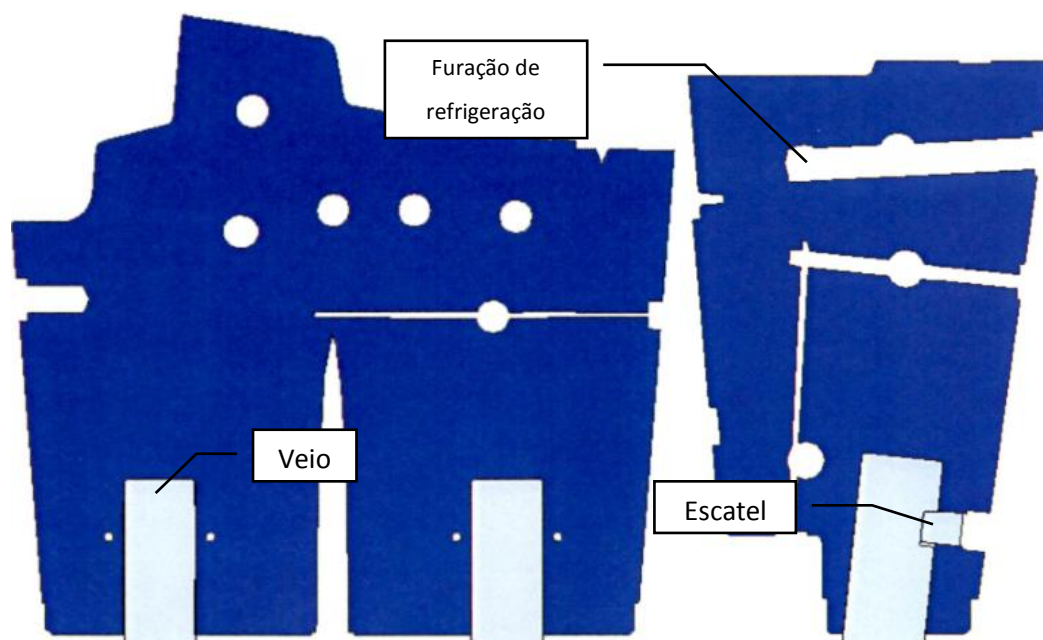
Vistas em corte de frente (esquerda) e lateral (direita) do movimento à extração SI10.
